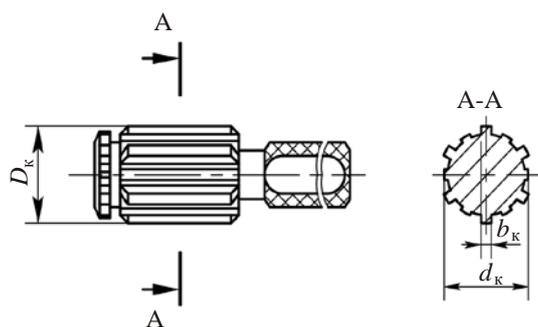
Измерительная часть шлицевого калибра-пробки
